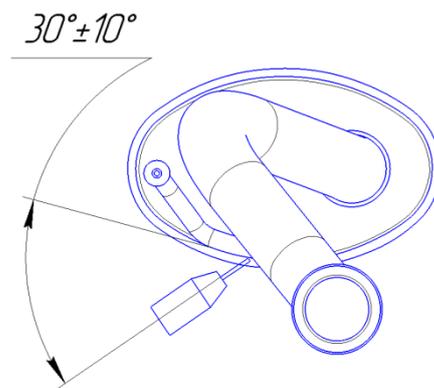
Сварка основного глушителя и кронштейна
